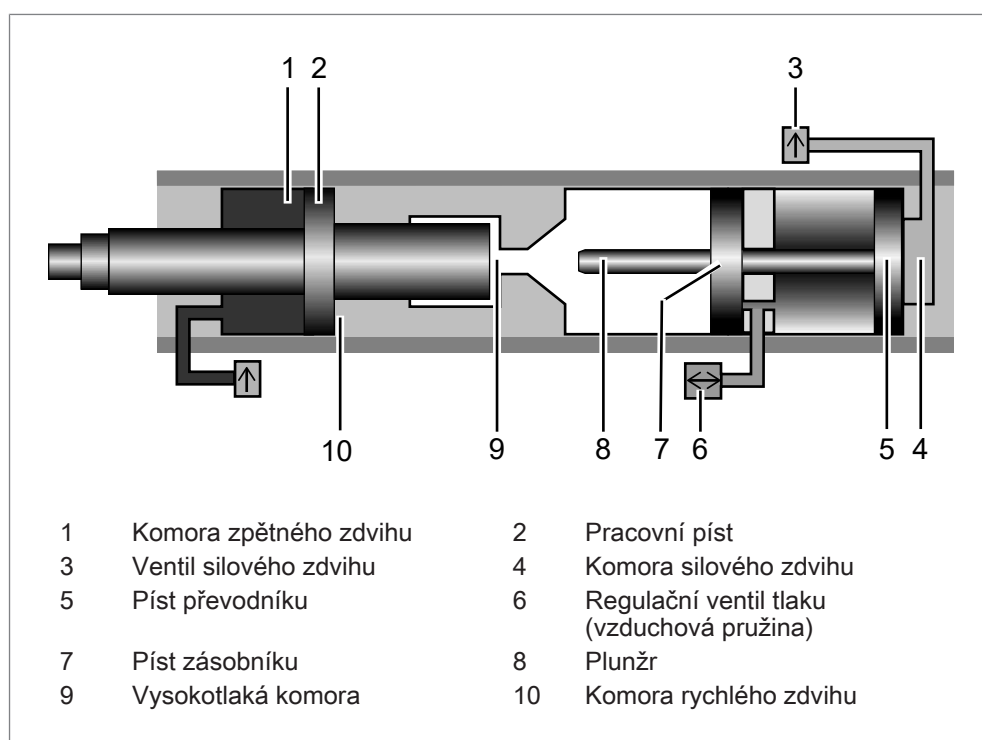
Zpětný zdvih Kraftpaket s mechanickou pružinou rychlého zdvihu
